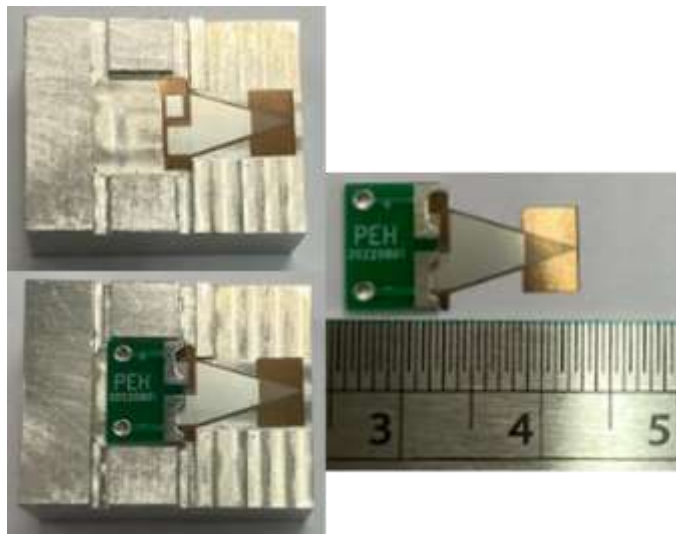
：焊接治具圖及焊接至 PCB 實體圖
